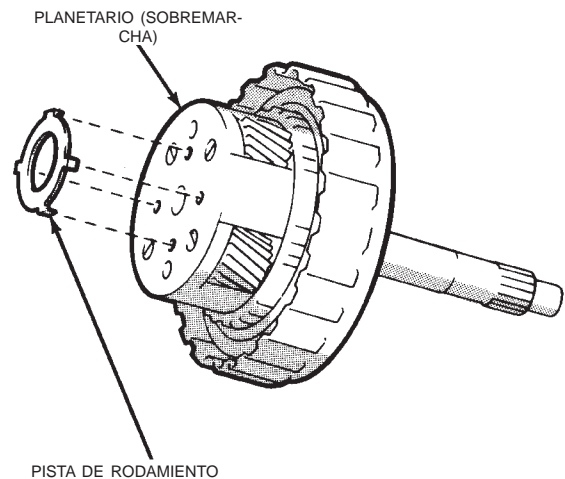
Desmontaje de la pista de rodamiento de la bomba de aceite
